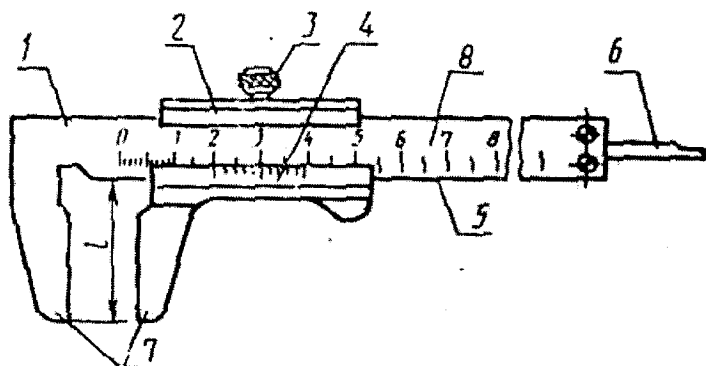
Штангенциркуль односторонній з глибиноміром з вимірювальними поверхнями із твердих сплавів:
